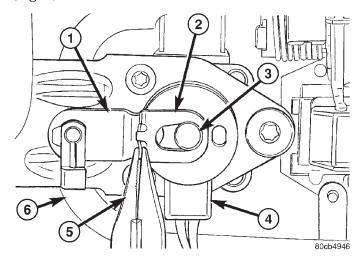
Desmontaje e instalación de retenedor de palanca de cilindro de cerradura
